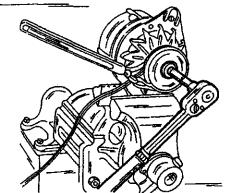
Отворачивание гайки с внутренней стороны ременного шкива. Наложить на ременной шкив клиновой ремень, как показано на рисунке.
